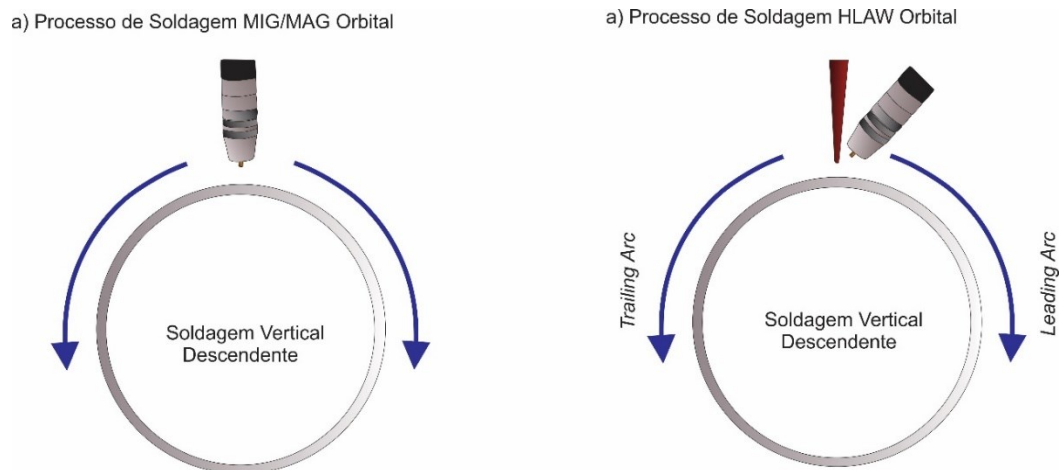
Alteração no sentido de alimentação de arame na soldagem orbital dos processos de soldagem (a) GMAW e (b) HLAW. (Fonte: Autor)
